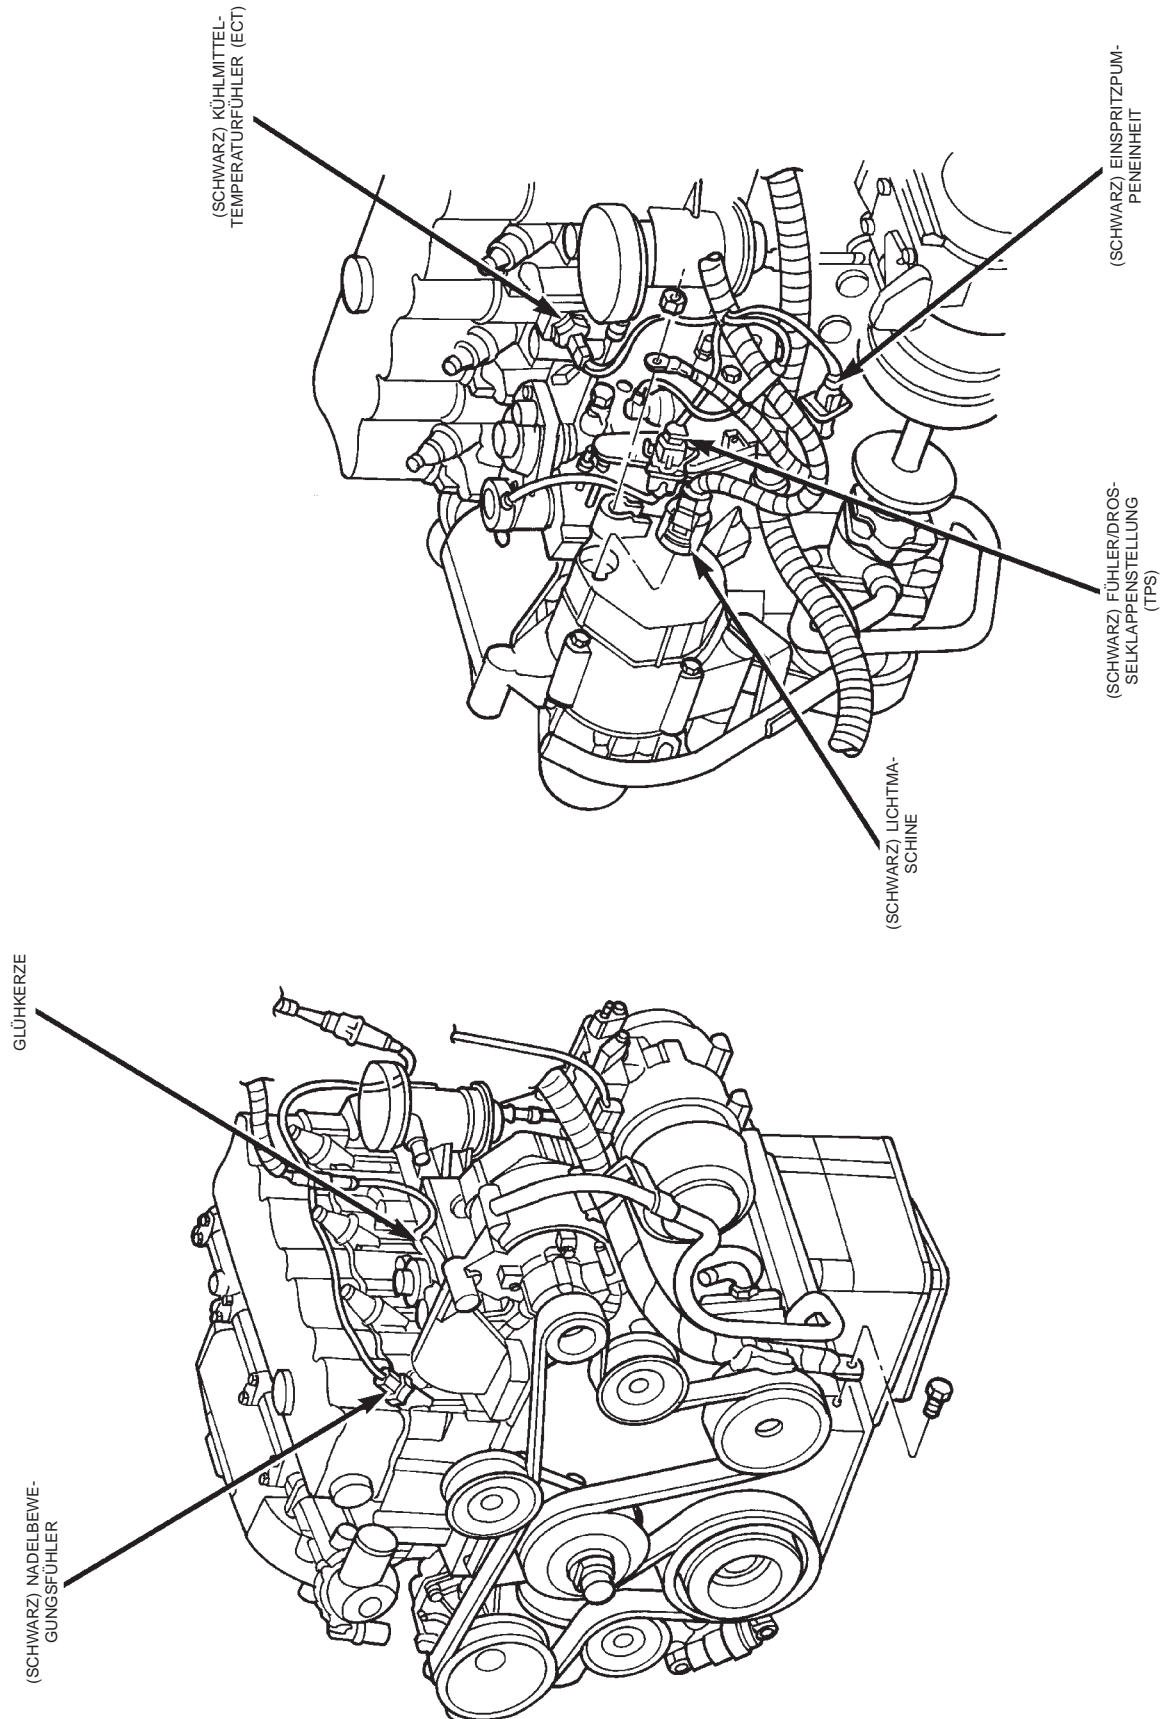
Motorraum rechts—Dieselmotor/Rechtslenker
